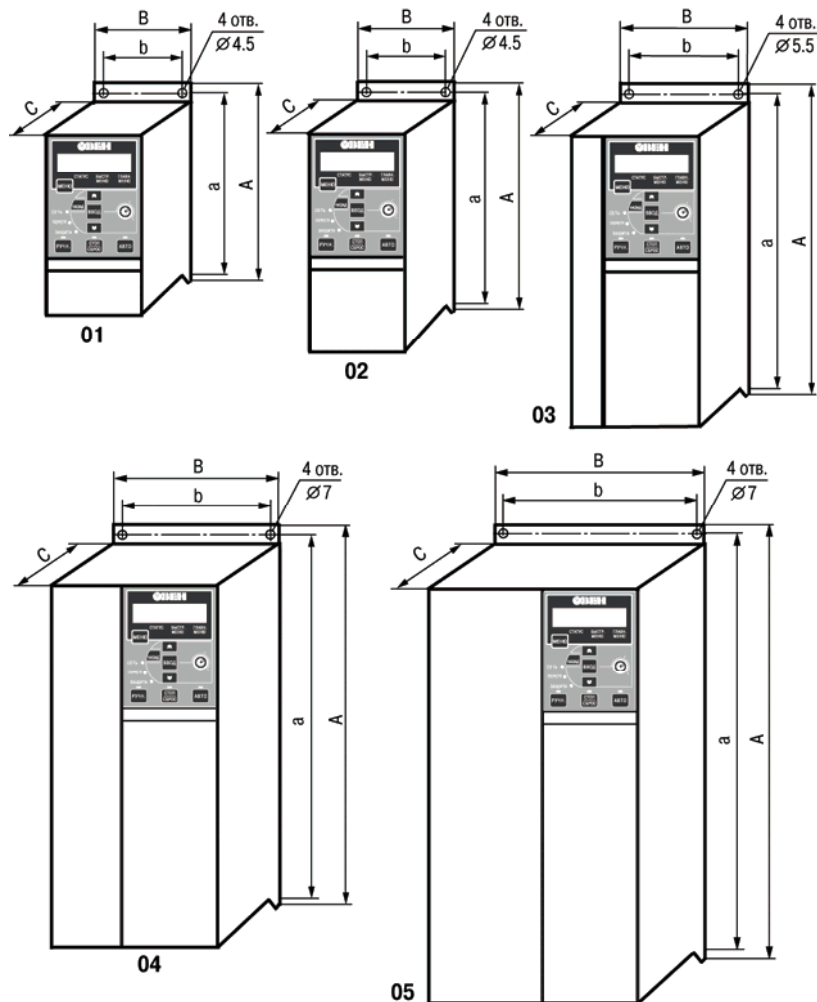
Габаритные и присоединительные размеры прибора с типоразмерами корпуса 01 – 05. Расшировка обозначений приведена в таблице А.1.
